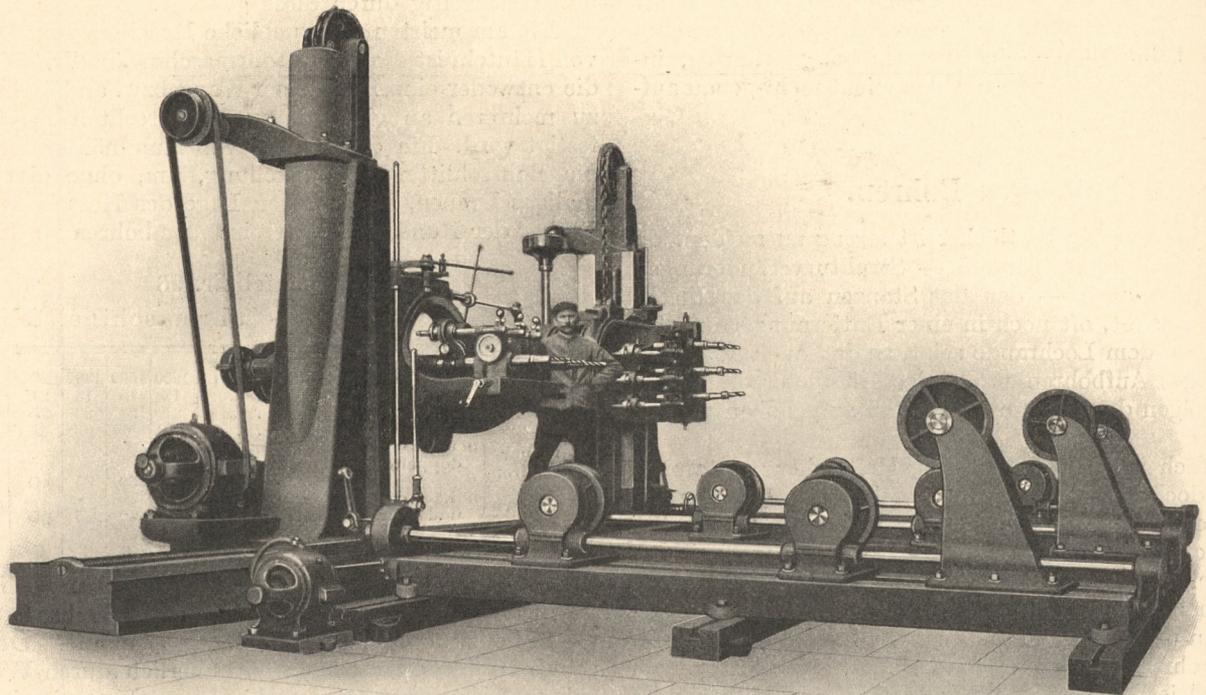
Doppelte Kesselbohrmaschine mit 6 Spindeln und Rollgang.
